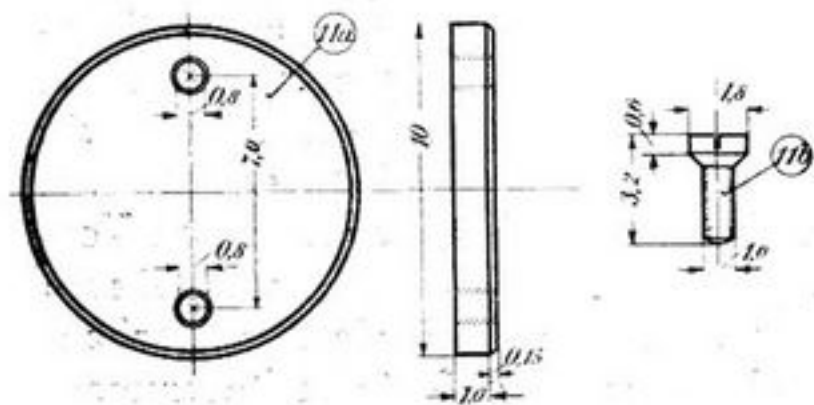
Untere Unruhdecke mit zwei Schrauben
